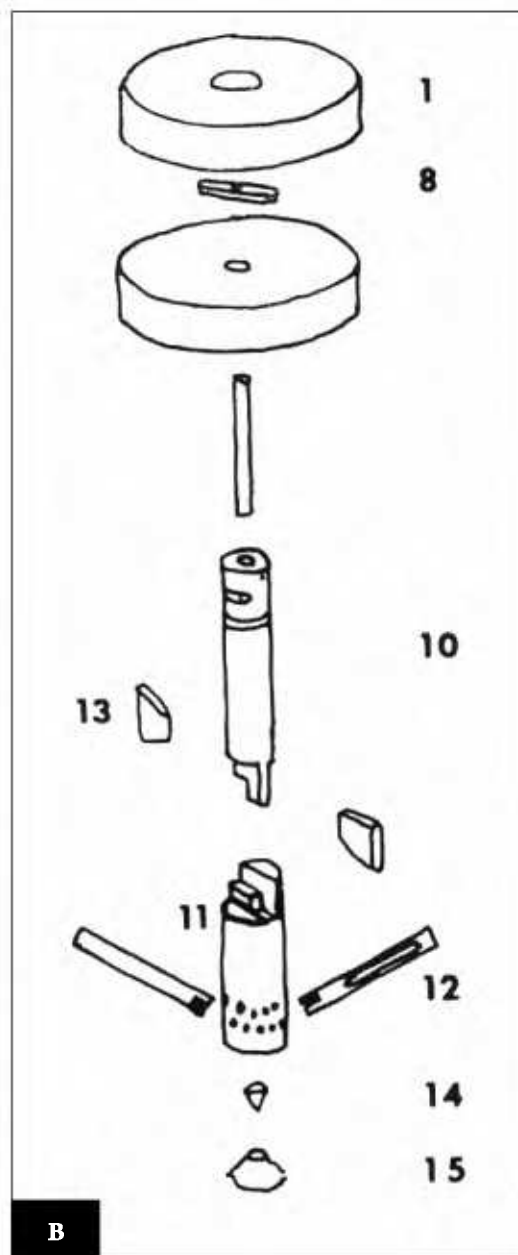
A-B : Le moteur hydraulique du moulin des Aït Mizan. D'après Cresswell, Moulin, 1987, p. 510, fig. 3, et p. 511). On distingue sous le roudet le banc de trempure horizontal.
